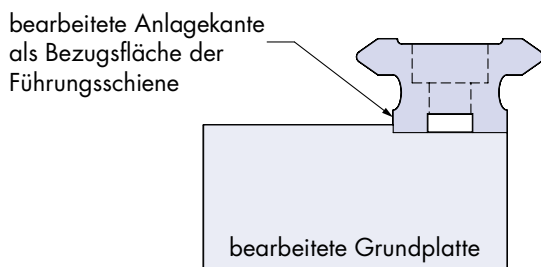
bearbeitete Bezugsfläche für die Ausrichtung der Führungsschiene
